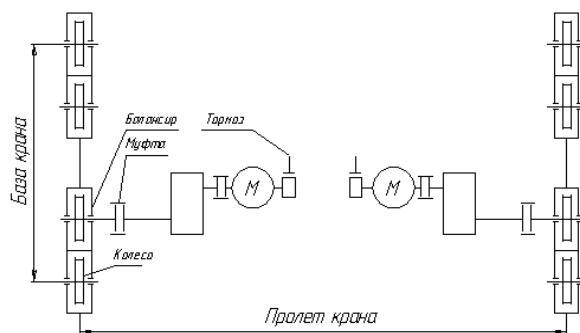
Предлагаемая кинематическая схема механизма передвижения
